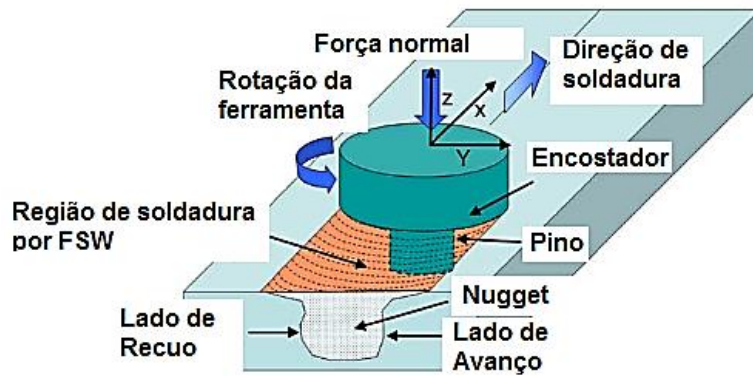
Esboço da técnica de Soldadura por Fricção Linear [33].
